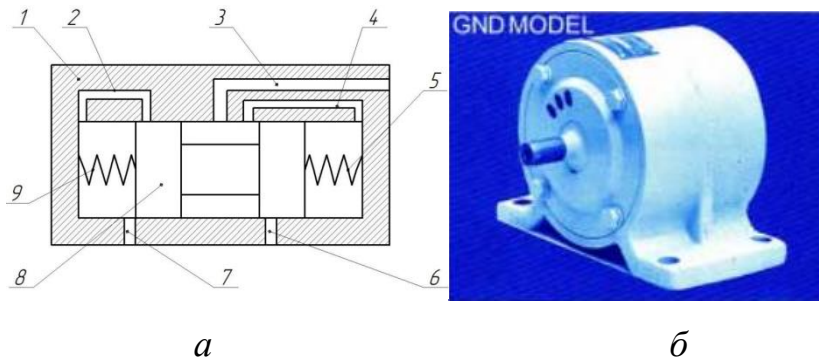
Пневматичний вібратор: а-схема; б-загальний вигляд.
